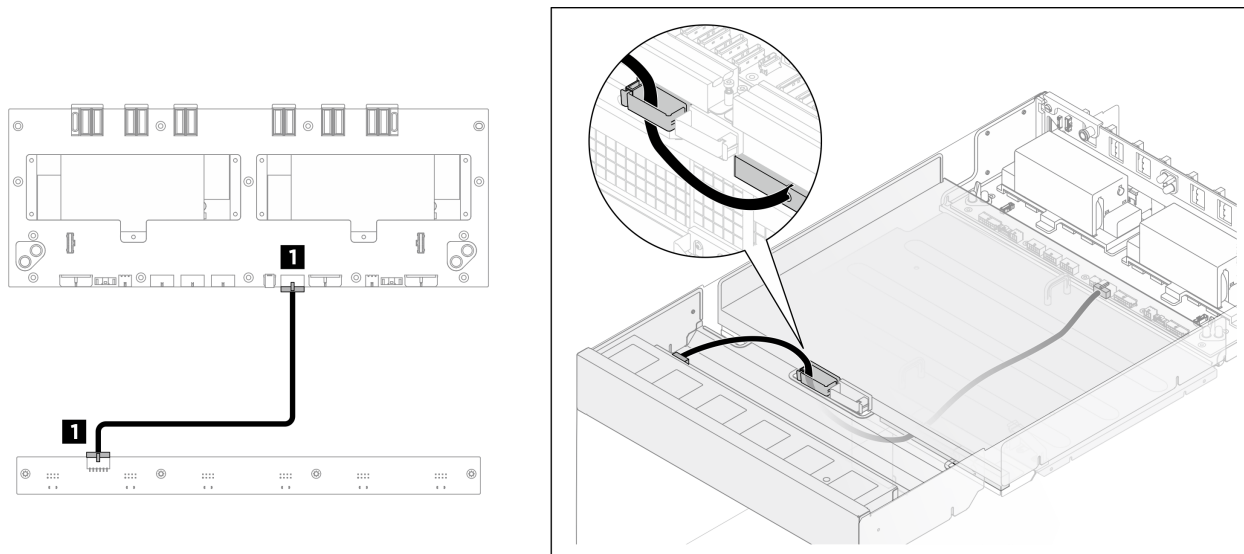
Disposición de los cables de la placa de control del ventilador frontal
